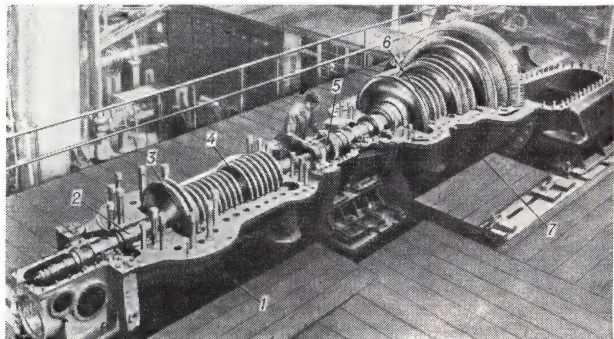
Двухкорпусная паровая турбина (со снятыми крышками): 1 — корпус высокого давления; 2 — лабиринтовое уплотнение; 3 — колесо Кертиса; 4 — ротор высокого давления; 5 — соединительная муфта; 6 — ротор низкого давления; 7 — корпус низкого давления.
